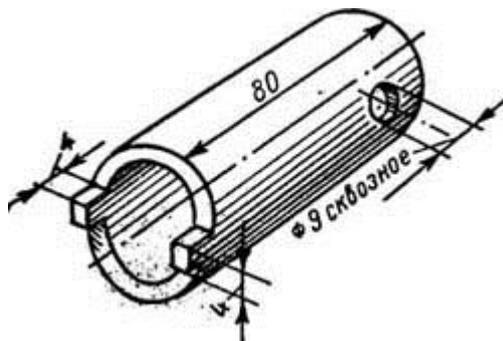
Ключ для гайки чашки подшипника рулевой колонки фары, руль и вывернуть верхние резьбовые пробки из перьев вилки
